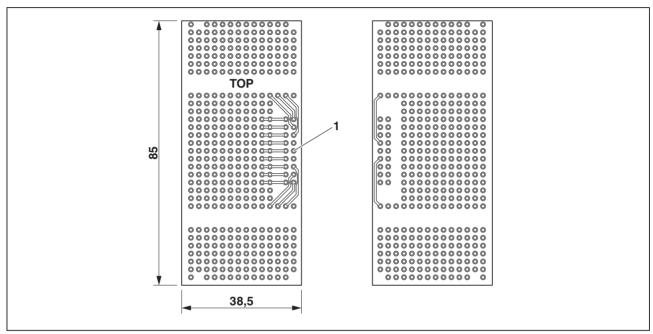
Abmessungen der Leiterplatte RPI-BC EXT-PCB HBUS SET, 2202995
